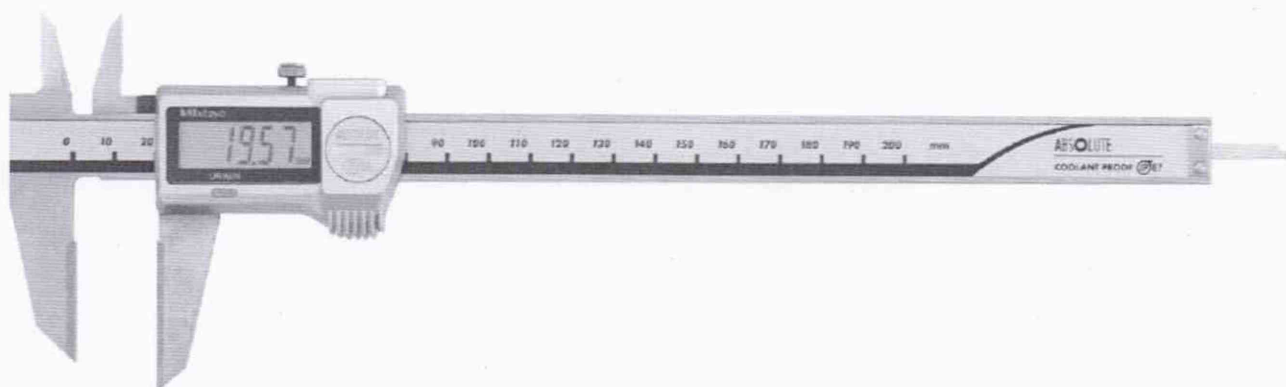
Общий вид штангенциркулей серии 573 модификации ABSOLUTE Digimatic с твердосплавными губками
